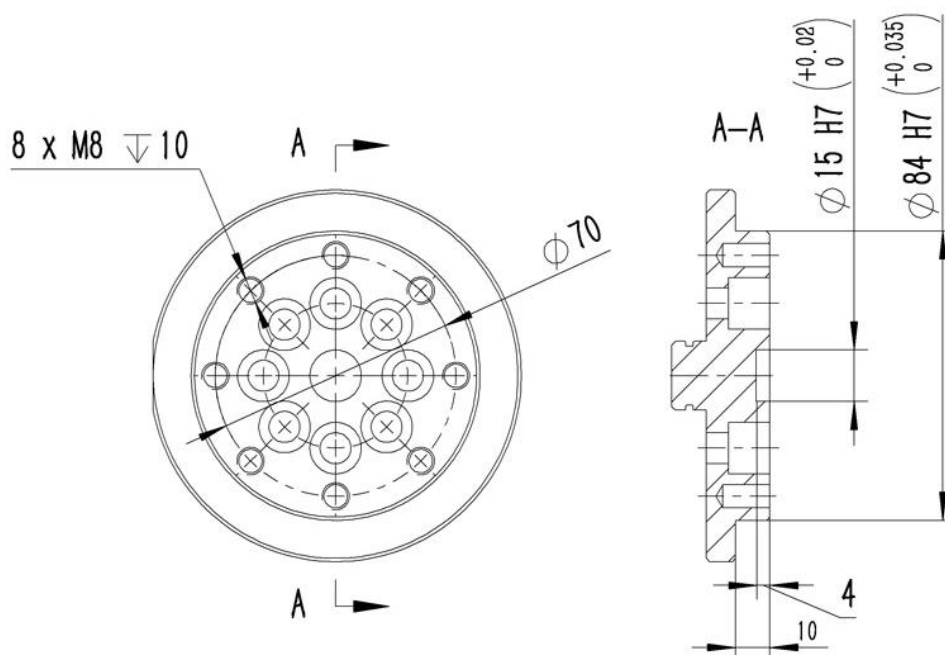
末端法兰尺寸 Diagram 2.10 Dimension of end flange
